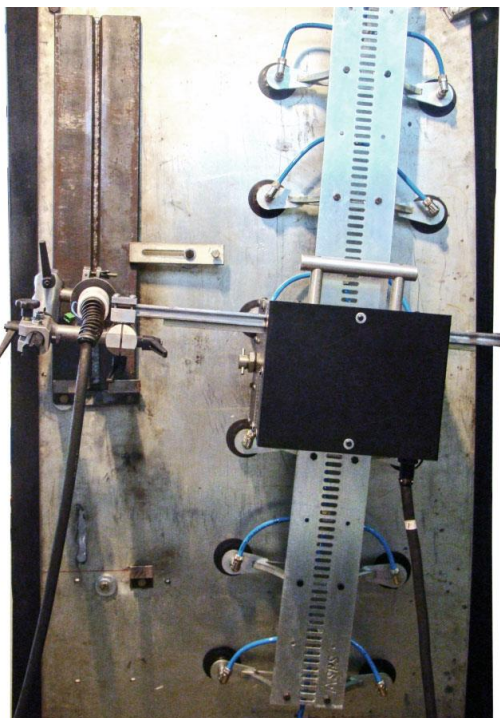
Manipulador robótico utilizado nos testes de soldagem fora de posição.
